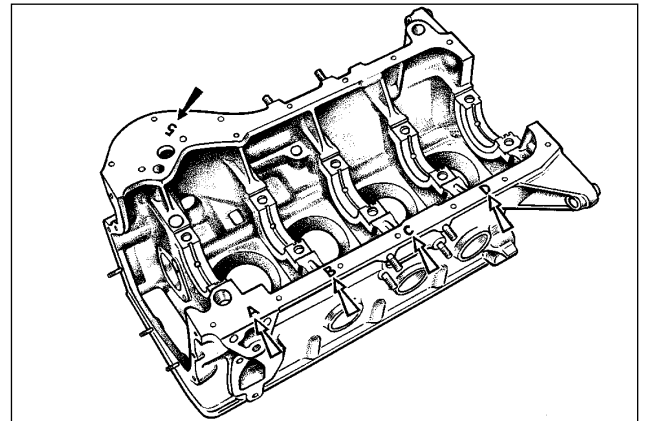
Markierung der Maßklasse der Zylinder an Zylinderblock
